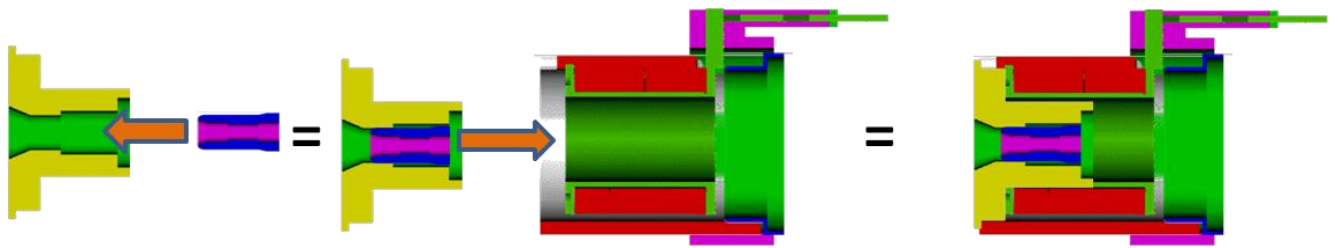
Ensamble rodamiento-núcleo magnético a grupo magnético.
